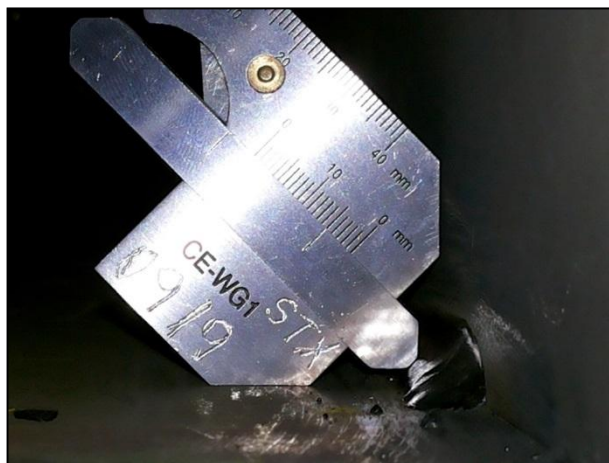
Dimensões dos corpos-de-prova - garganta de solda uniforme e igual a 5mm.
